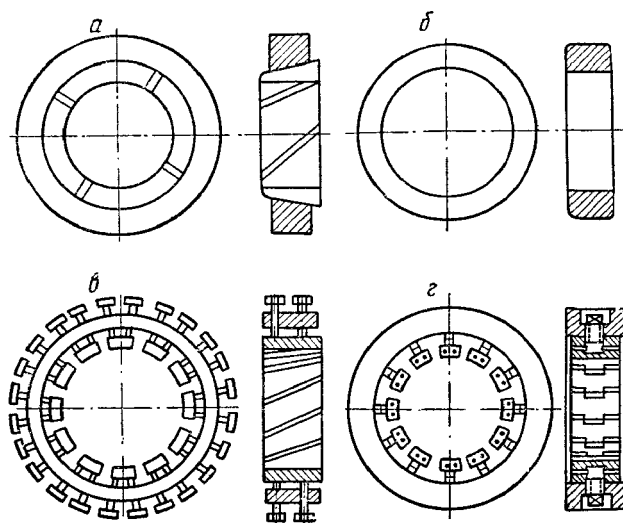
Кольца для прессовки комплекта пластин коллектора:
